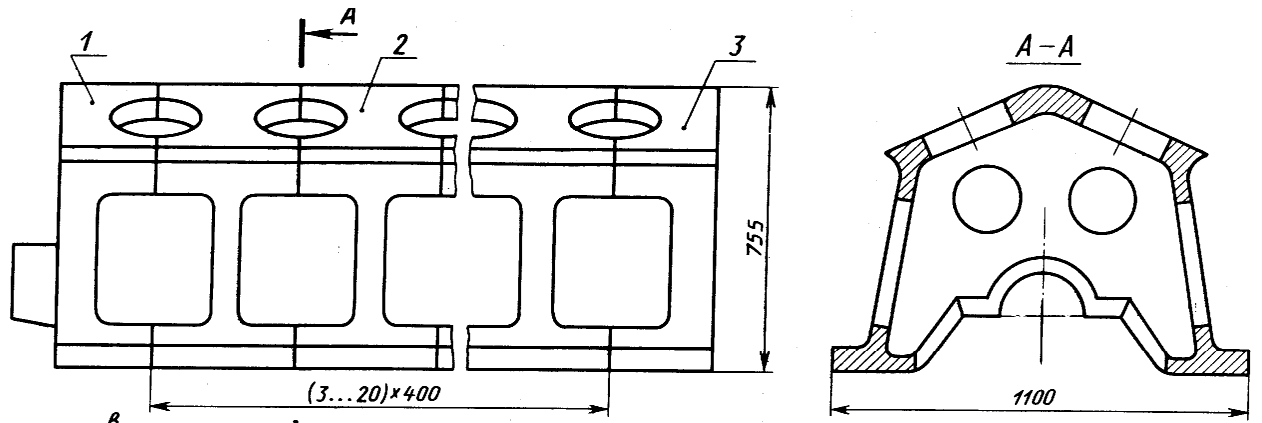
Конструкция сварно-литого блока цилиндров
